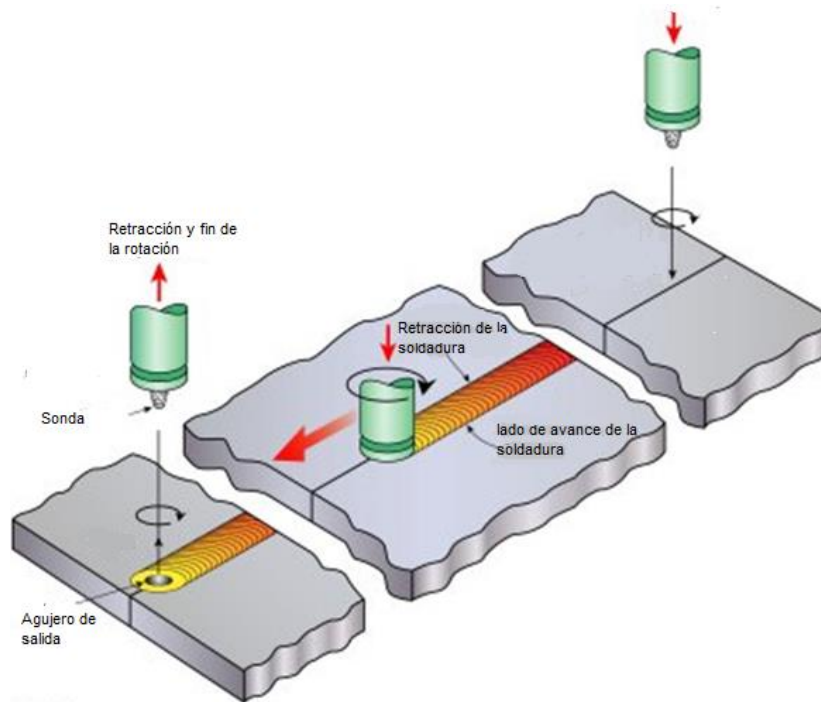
Proceso de soldadura por fricción-agitación (FSW). [10]
